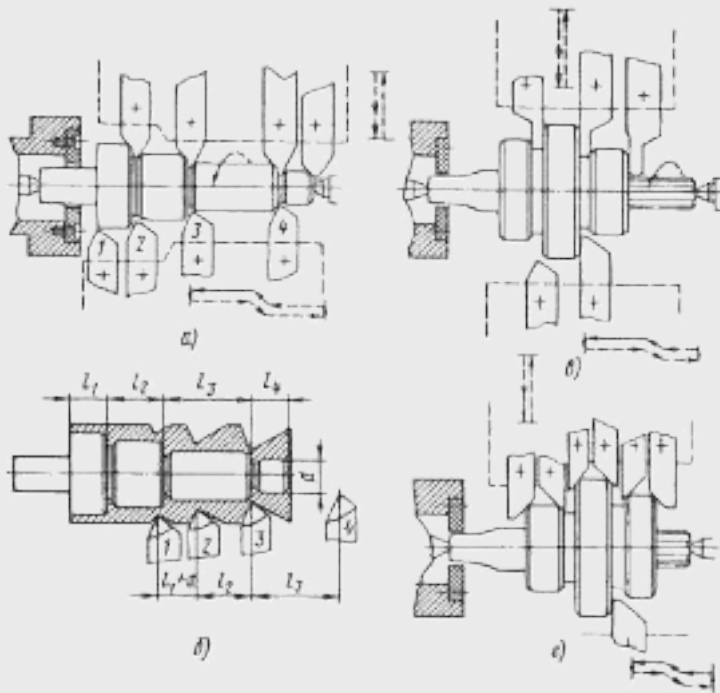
Типові схеми обробки заготовки на багаторізцевому токарному автоматі 1730: а — різці в кінцевих положеннях; б — установлення різців і зони їх врізання; в, г — схеми обробки однієї заготовки за дві послідовні операції
